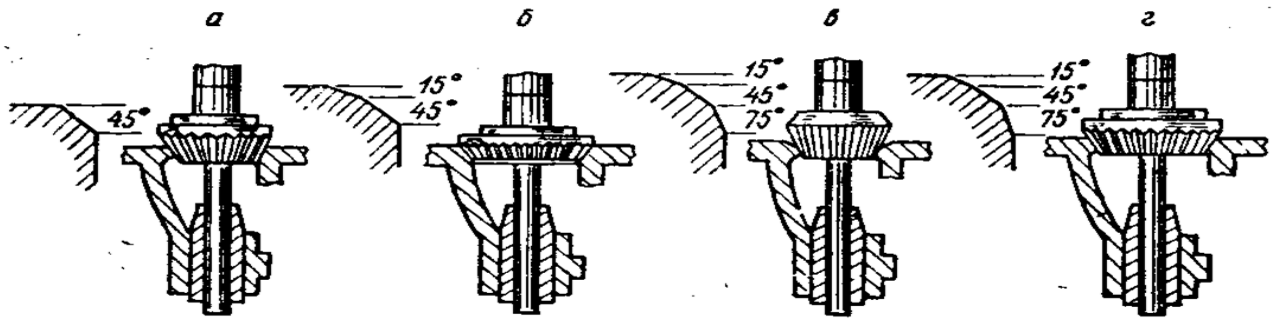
Обробка клапанного гнізда фрезами. Фрезерування під кутом:
